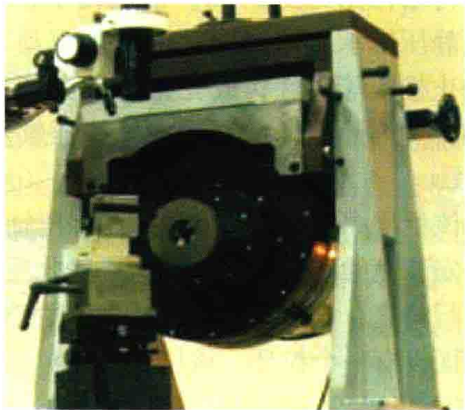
套装空气静压轴承行星运动机构在圆弧刃金刚石刀具刃磨机上的应用
